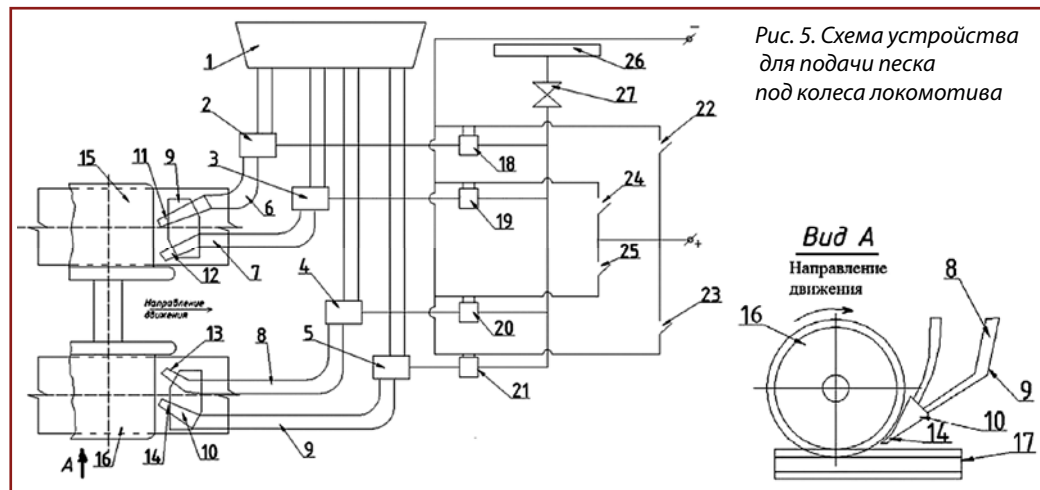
Схема устройства для подачи песка под колеса локомотива
